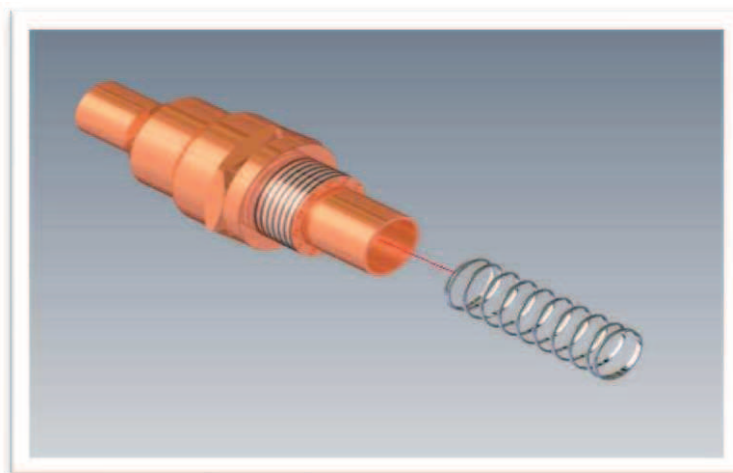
Inserción del resorte de compresión al conjunto: tuerca unión-reducción-cuerpo de la válvula.
